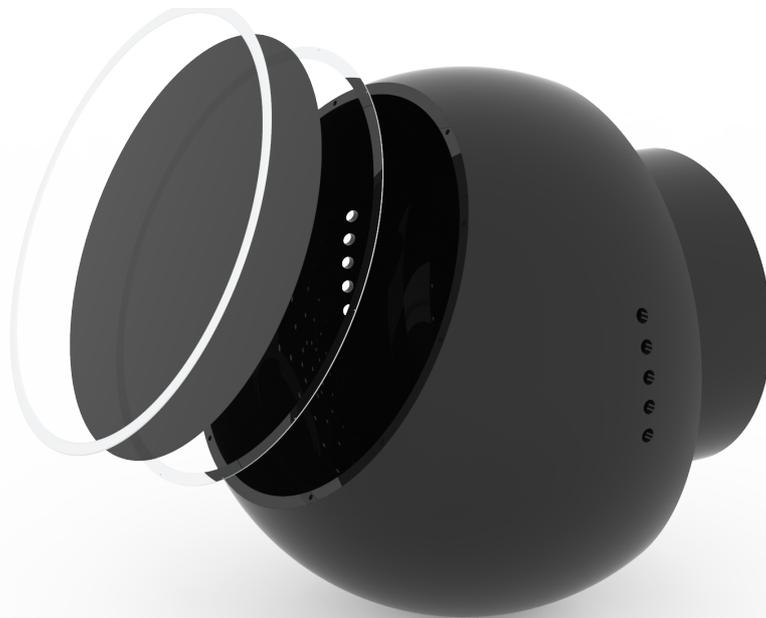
Render 6 de ACCOM One con el cuerpo montado y explosión de las piezas adicionales
